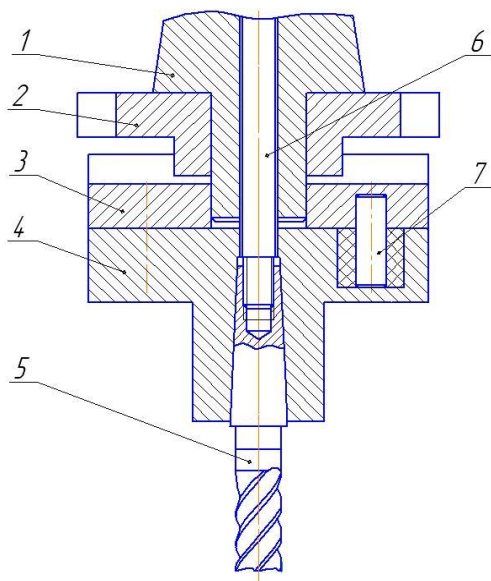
фрезерная оправка с демпфирующими элементами для концевой фрезы: 1-оправка; 2-планшайба; 3-верхнее кольцо узла демпфирования; 4- нижнее кольцо узла демпфирования; 5-фреза концевая; 6- штанга; 7-штифт с резиновой вставкой (демпфирующий элемент).
